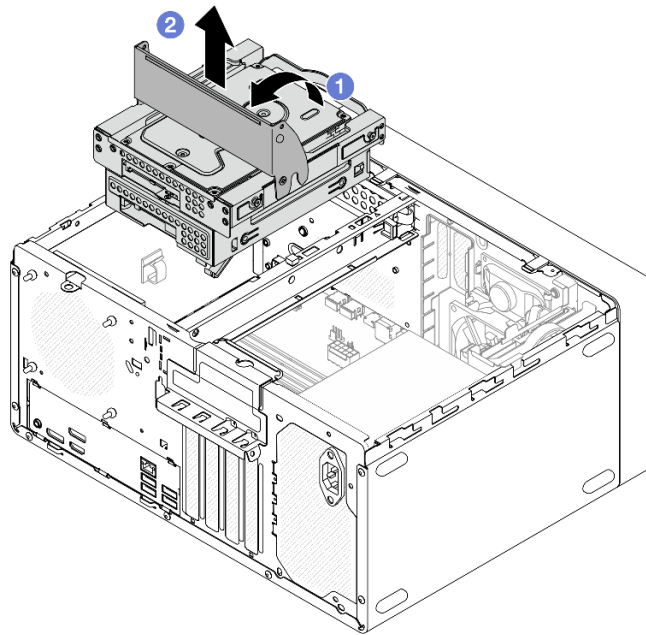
Entfernen der Laufwerkhalterungsbaugruppe für Position 2 + 3
